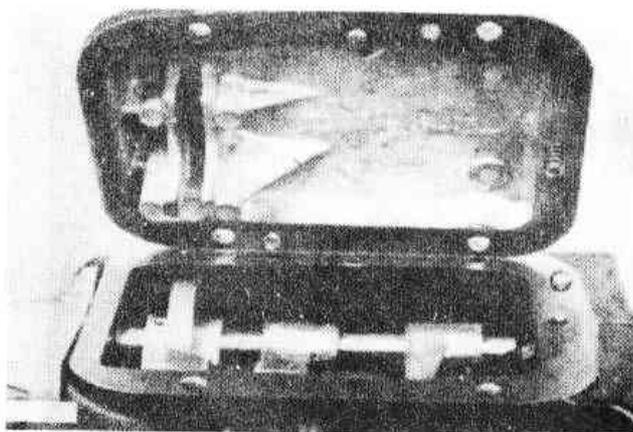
Снятие верхней крышки — коробка передач типа С. Обратите внимание на местоположение пружины и шарика (Разд.3 и 7).
